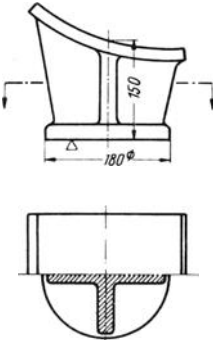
Werkzeugzeichnung für einen Kesselfuß.
